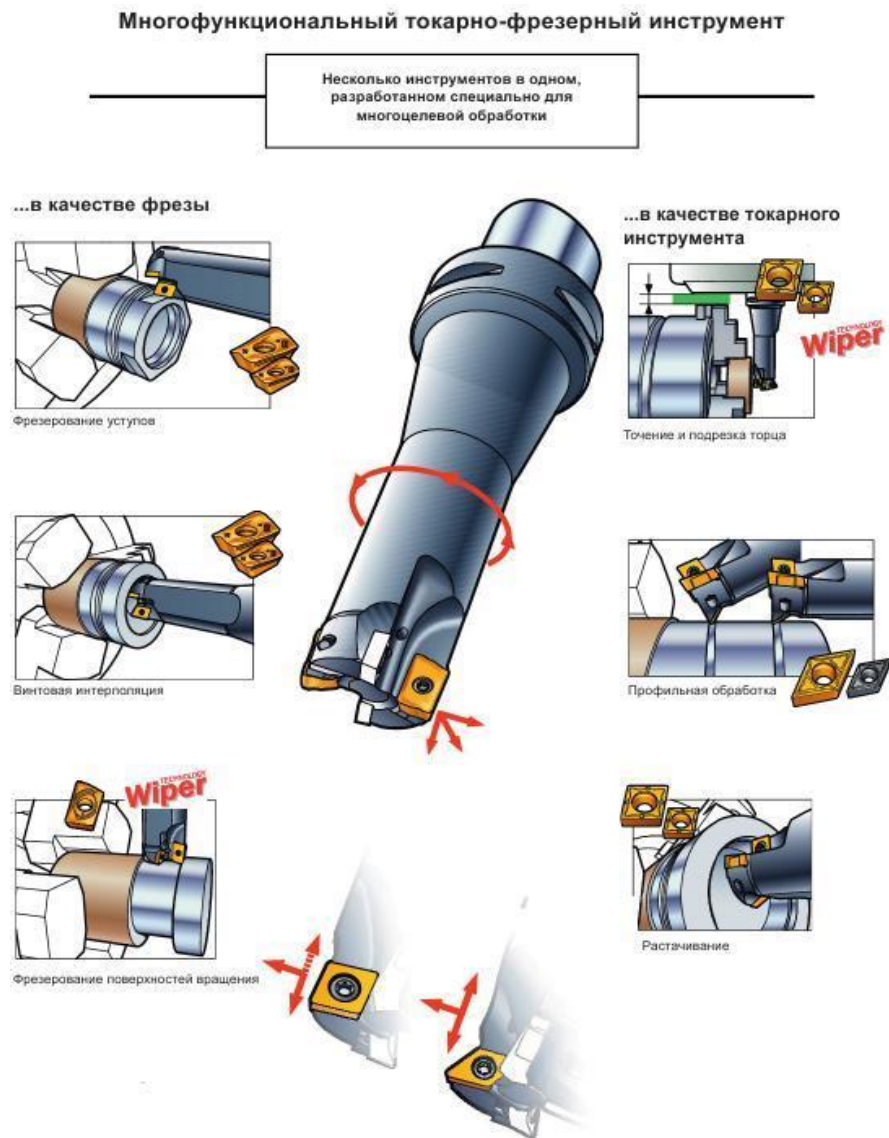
Токарні інструменти оптимізовані для багатоцільової обробки.
